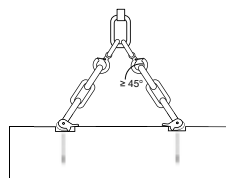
Rein axiale Belastung der Schraube durch passgenaue Fräsungen
